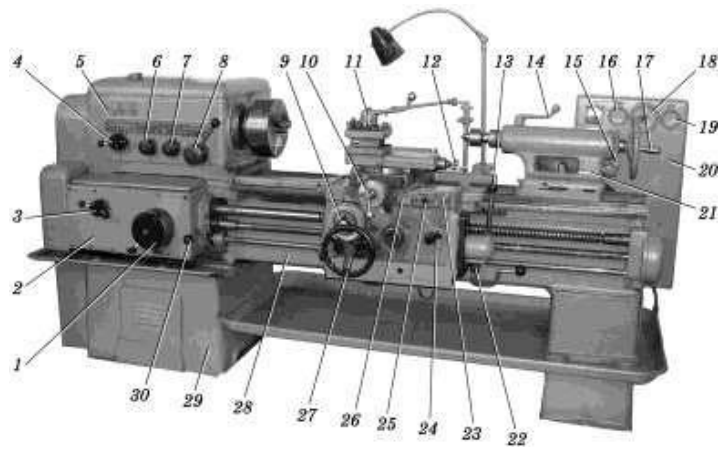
Загальний вигляд токарно-гвинторізного верстата 1К62
